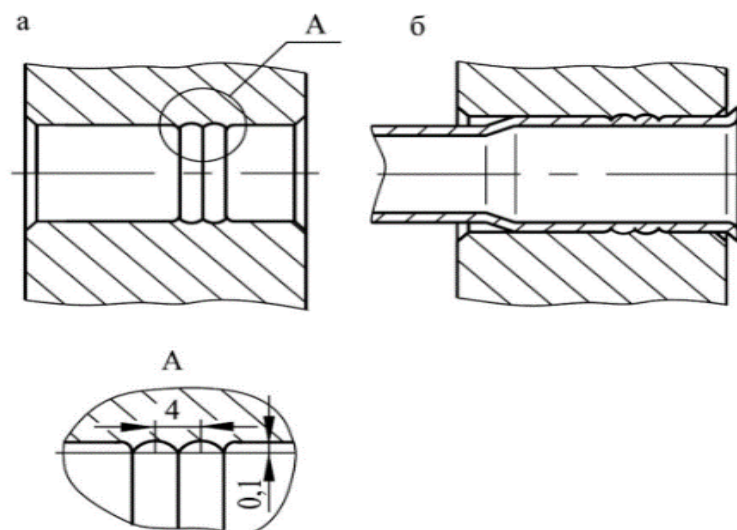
Способ крепления трубок в трубных досках: а – отверстие с кольцевыми рельефами в трубной доске, б – развальцовка трубки в отверстии с кольцевыми рельефами
